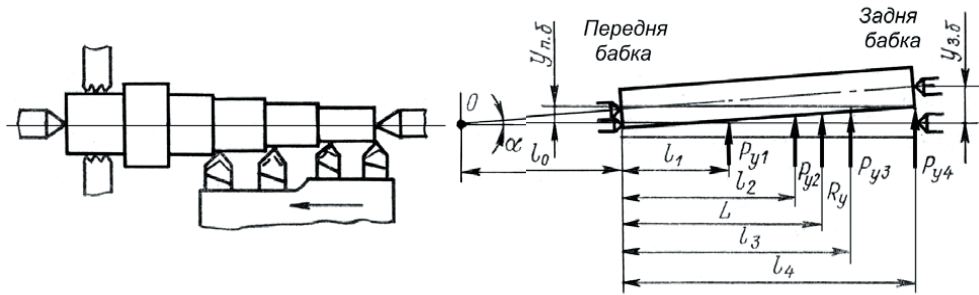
Виникнення похибок форми і розмірів при багаторізьцовій обробці
